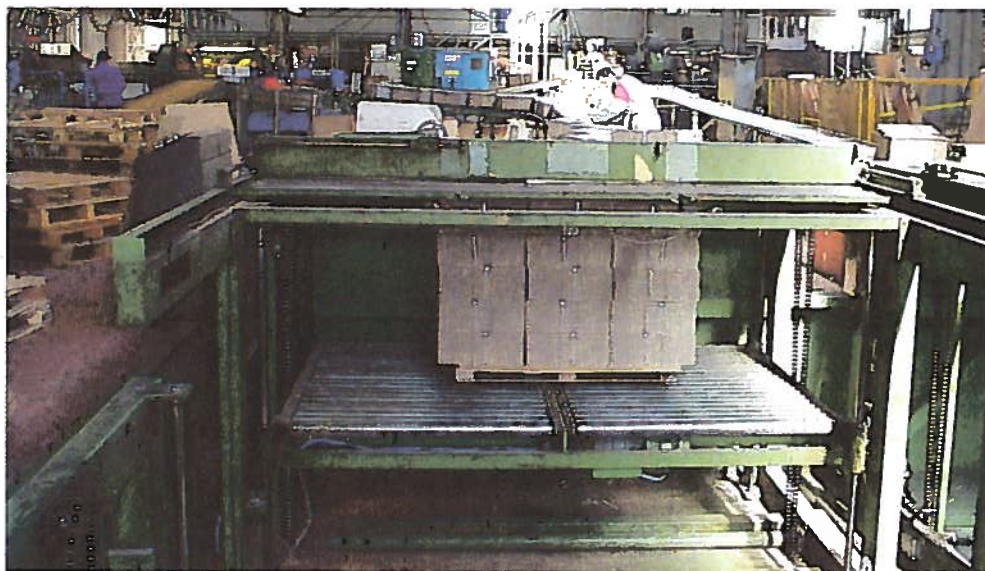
Pallettizzatore semiautomatico a buca nel pavimento, con addetto al lavoro.
